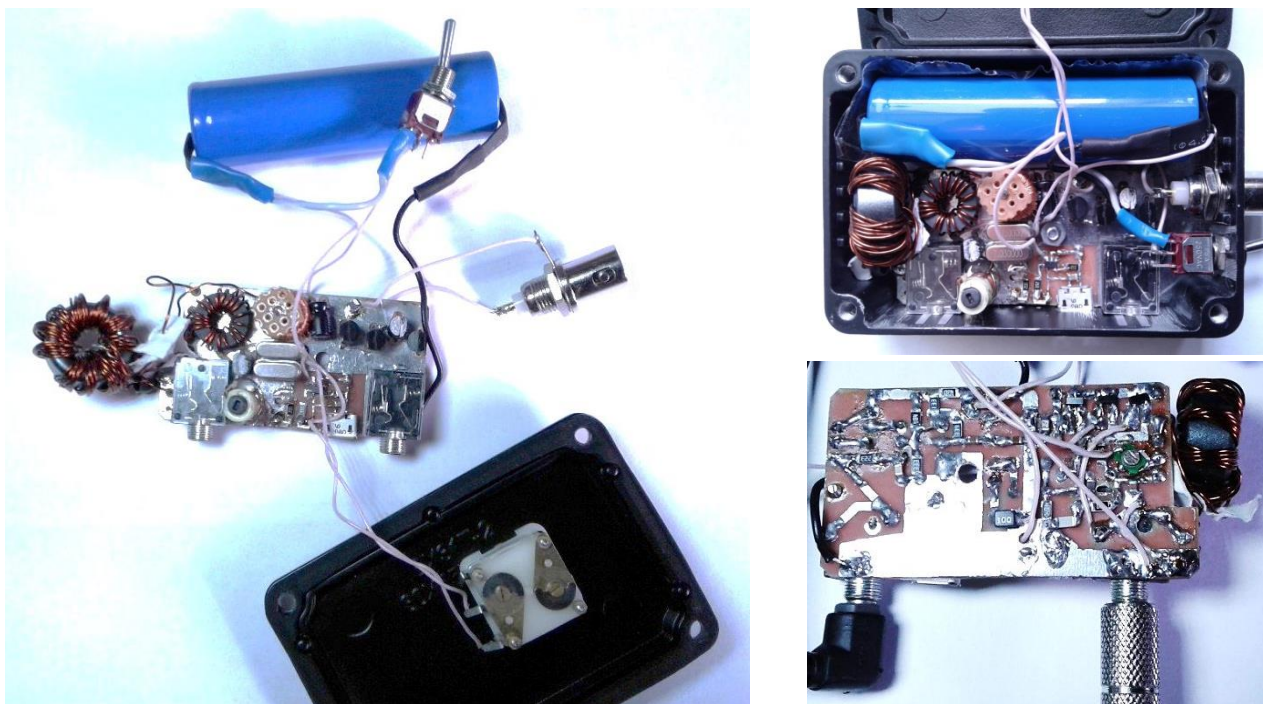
Конструкция и внешний вид низковольтного трансивера.
